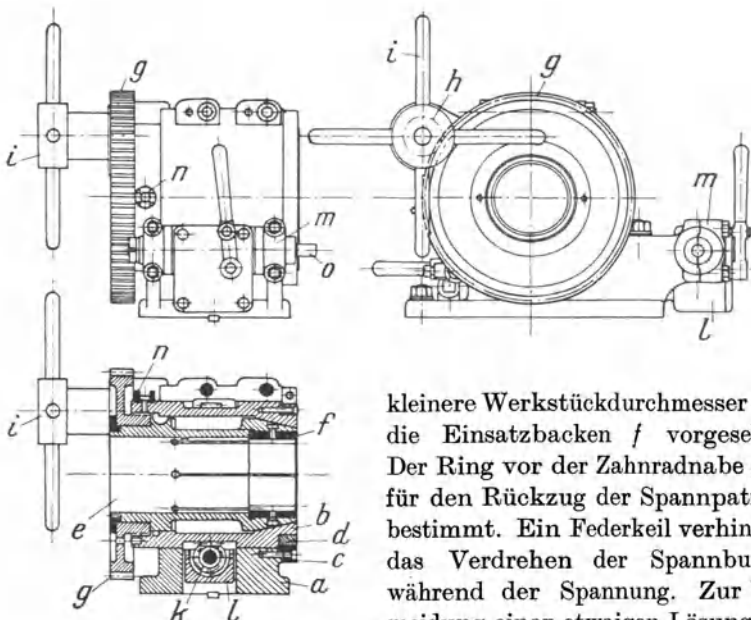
Gewinde-Fräsvorrichtung, speziell für Universalfräsmaschinen.
